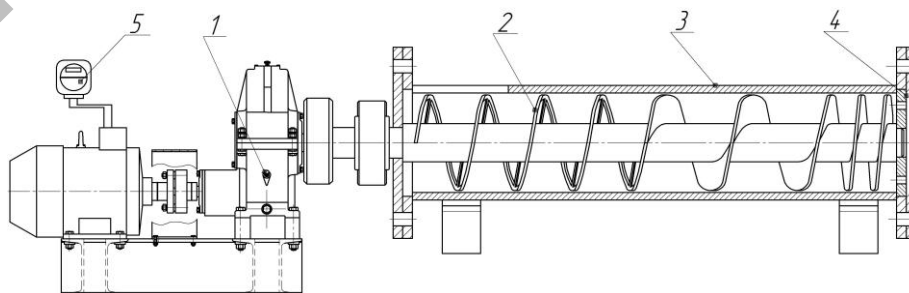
Экспериментальная установка непрерывного действия для замеса теста: 1 - привод; 2 - рабочий орган (шнеки); 3 - корпус; 4 - стабилизирующая решетка; 5 - прибор "VOLTcraft" для измерения электрической мощности.
